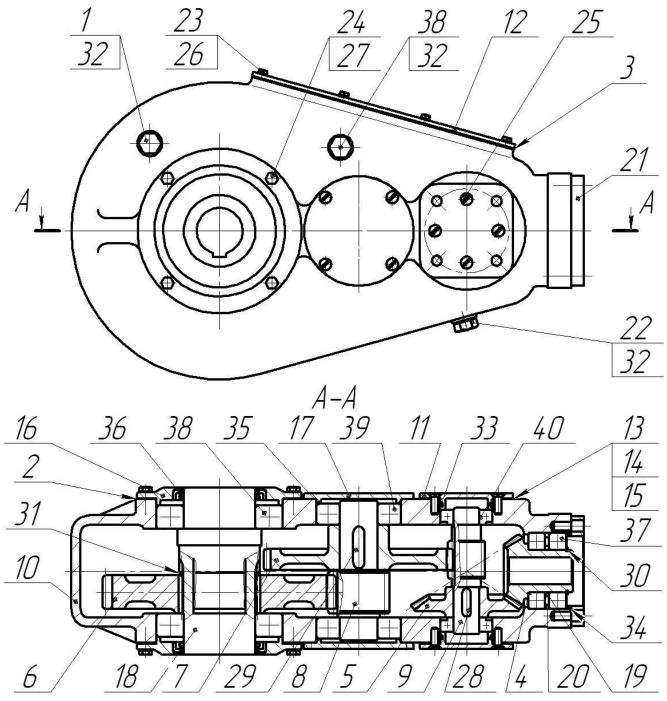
Редуктор (МТУ-13.16.05.000)
